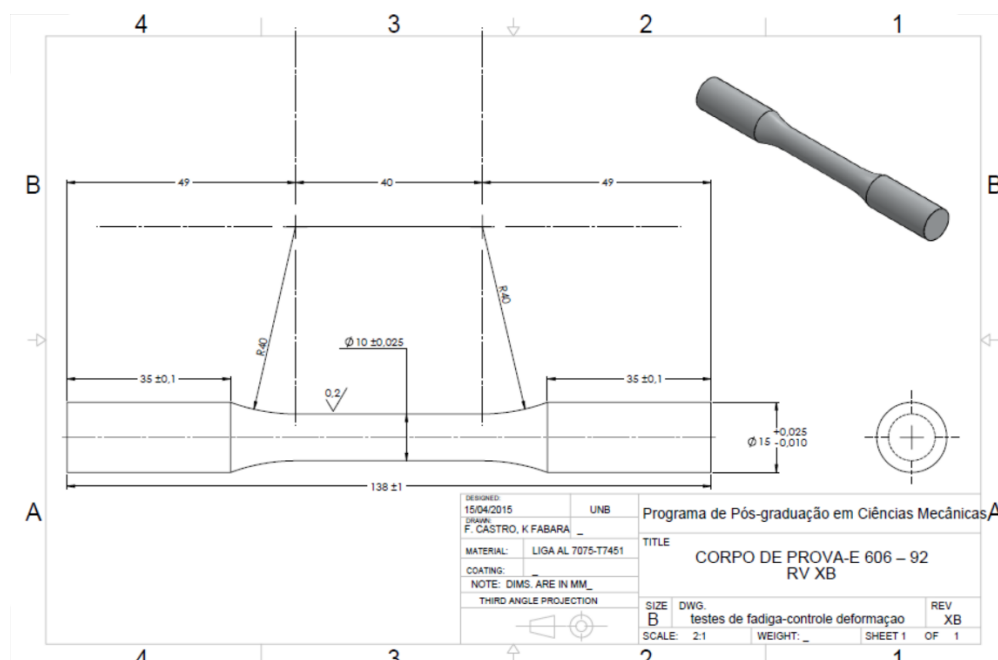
Desenho técnico do corpo de prova sem entalhe.
